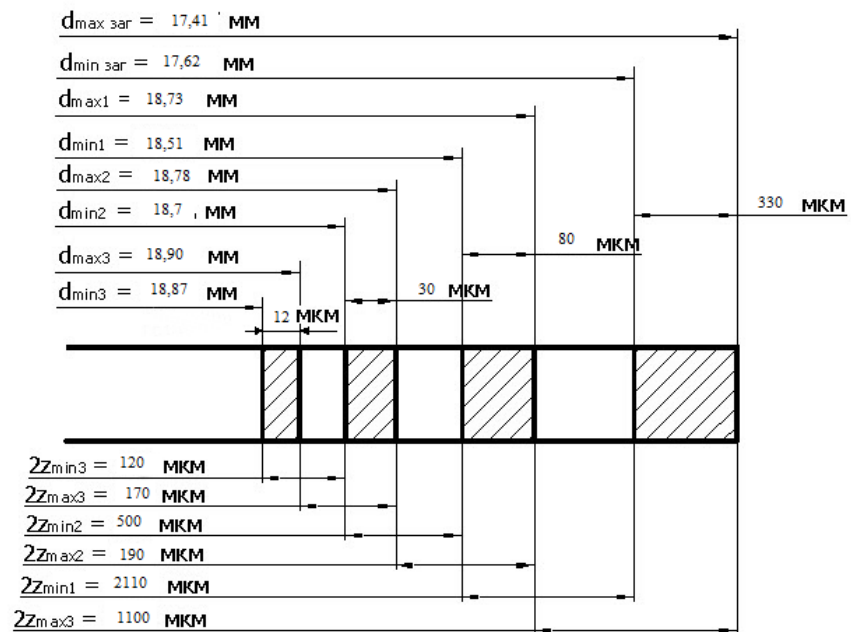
Схема розміщення припусків та допусків на поверхню штока з діаметром $\varnothing 106H7$
